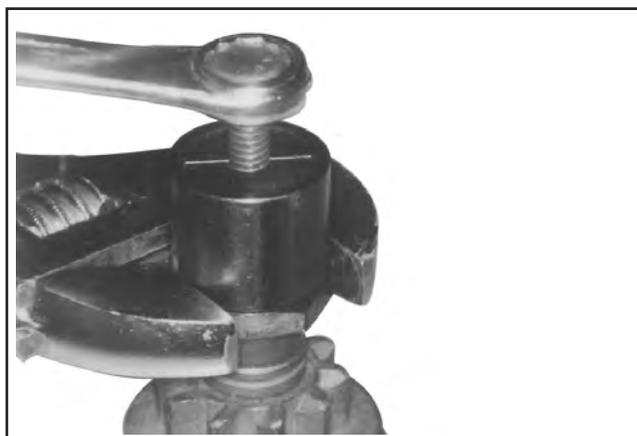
Dichtung des Werkzeugs und Drehung der mittleren Schraube (Uhrzeigersinn) für die Entfernung des Halterings.
